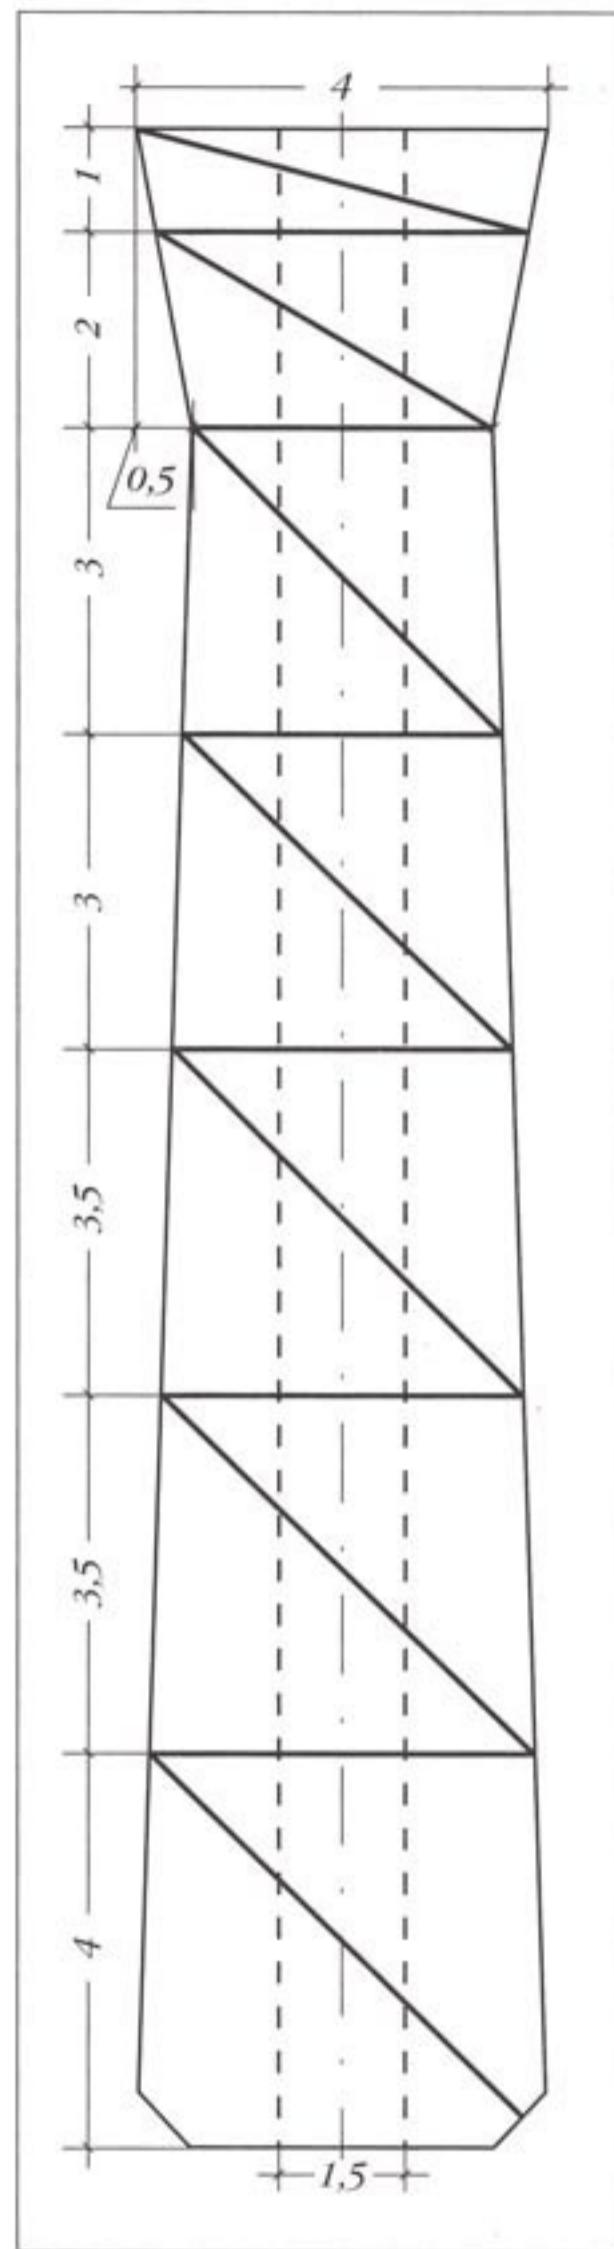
Схема разметки стойки подсвечника к рис. 159
